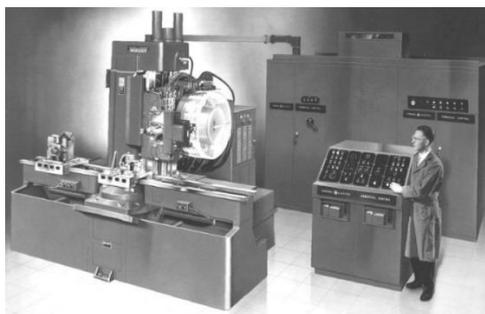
Máquina fresadora CNC creada en el MIT en 1958.
